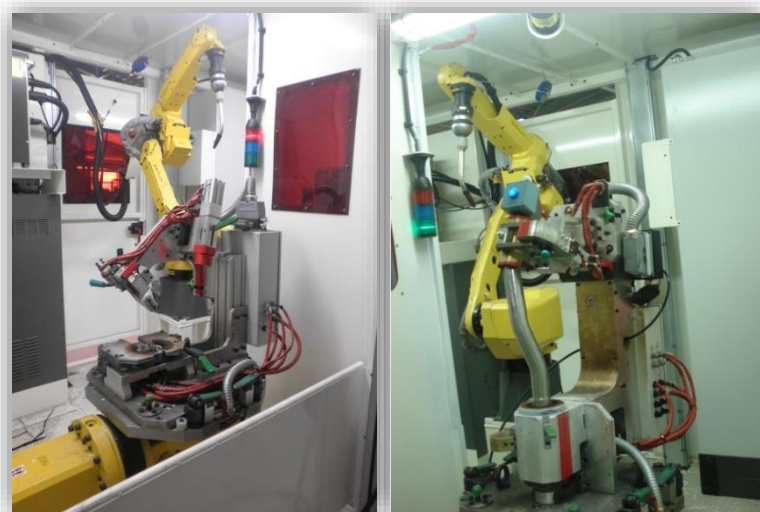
Equipamento: Soldadura do Flexível
